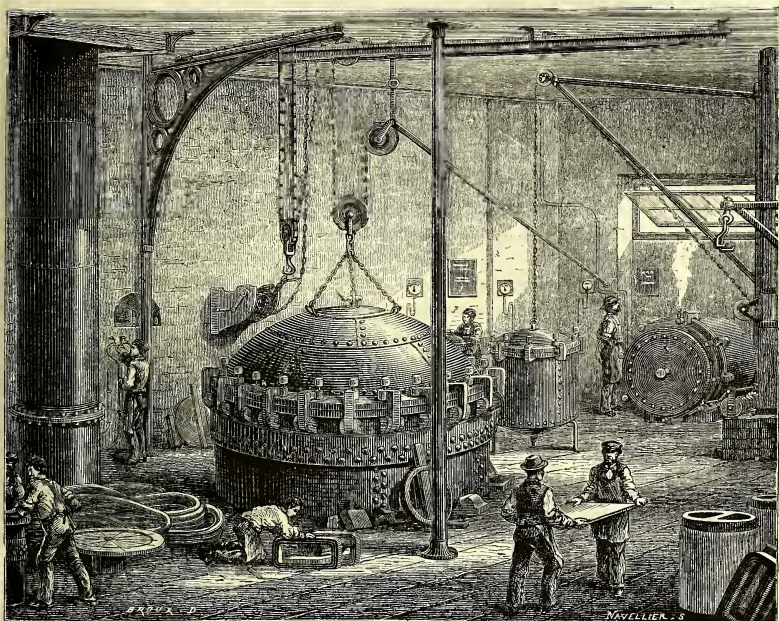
Chaudières pour vulcaniser le caoutchouc par la vapeur humide.
